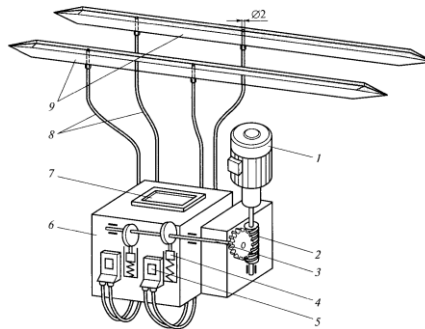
Схема автоматичного змазування напрямних: 1 – електродвигун; 2 – черв'як; 3 – вал; 4 – плунжер; 5 – оглядове вікно; 6 – корпус насоса; 7 – кришка; 8 – трубки; 9 – напрямні
